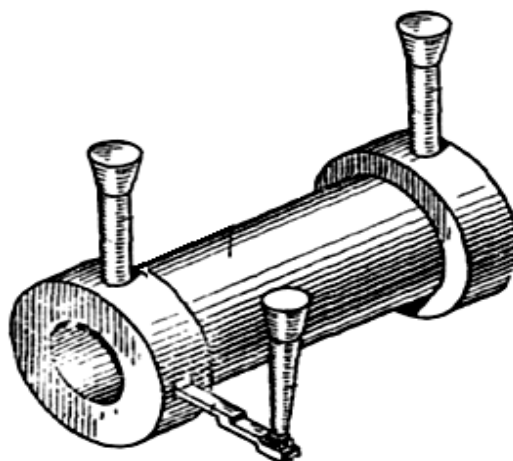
Отливка с элементами литниковой системы после выбивки
